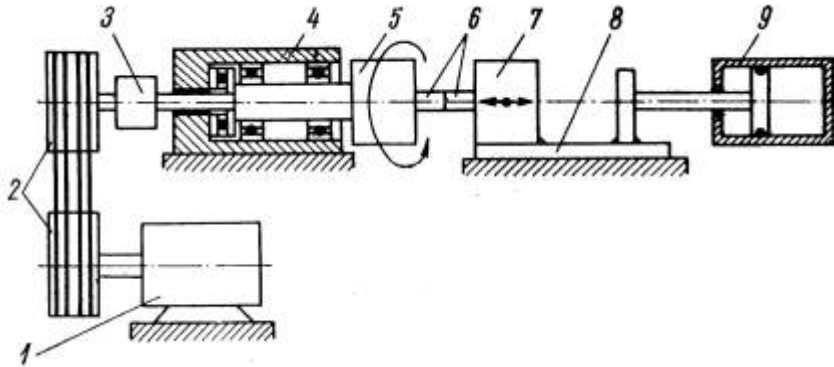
Принципова конструктивна-кінематична схема установка СТ110 для зварювання тертям:
